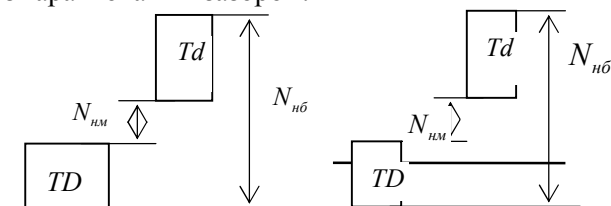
Схеми розташування полів допусків посадки з гарантованим натягом.
